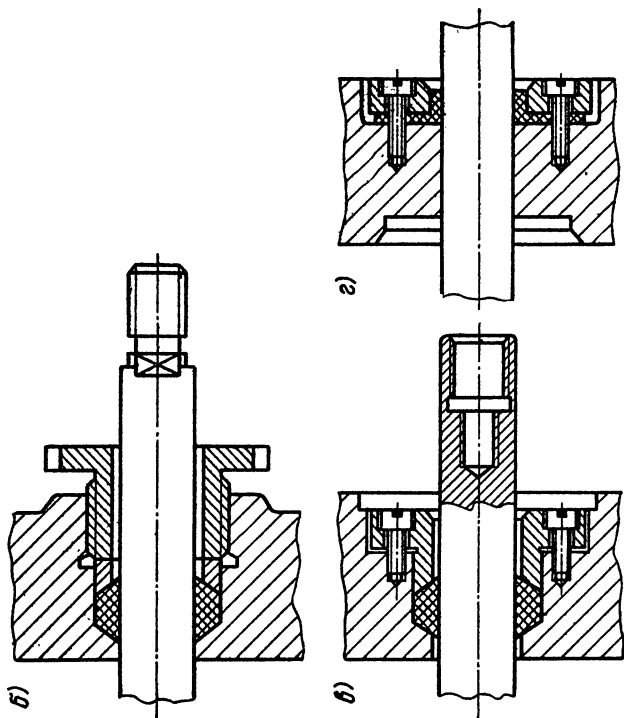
Сборка гидроцилиндра и способы уплотнения штока
